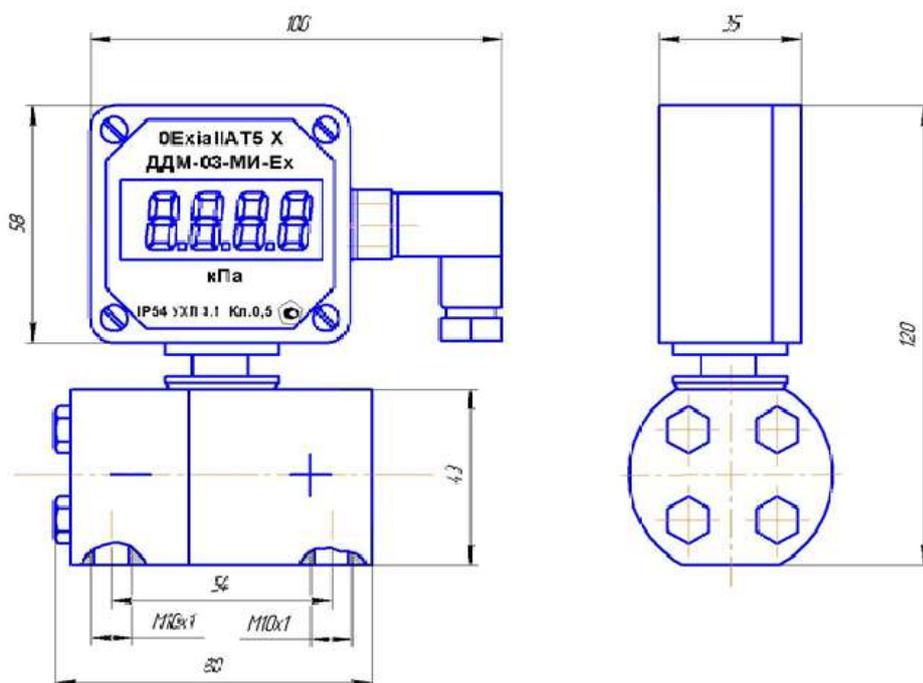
Габаритные и присоединительные размеры датчика ДДМ-03-ДД-МИ-Ех
